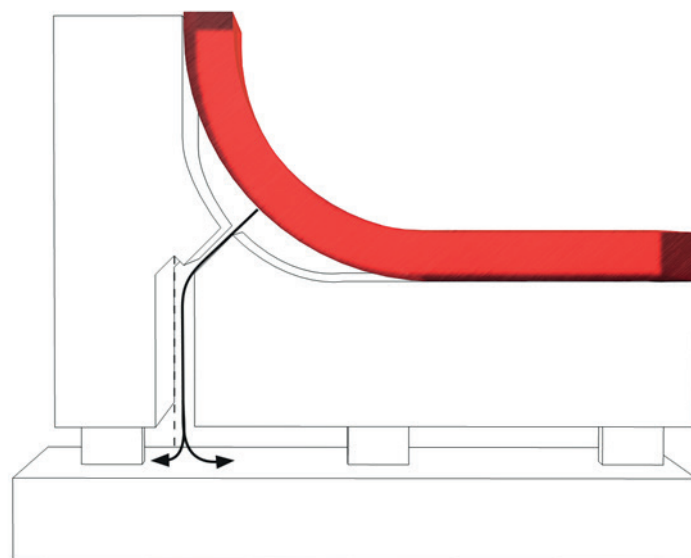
Entlüftungsbohrung an Formwerkzeug
